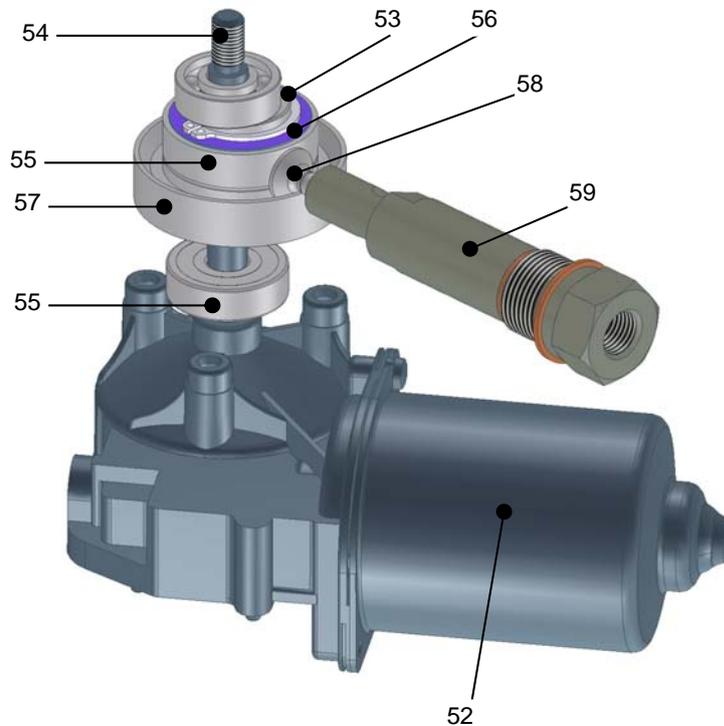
(Pumpenmechanik - Baugruppe Getriebemotor und Exzenter)
